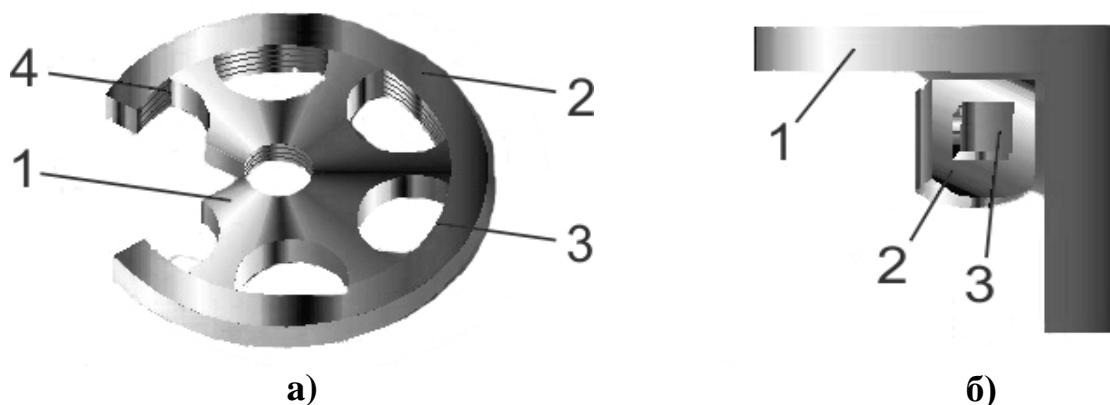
Фторопластовий тримач для закріплення зразка (а): 1 – підставка;
